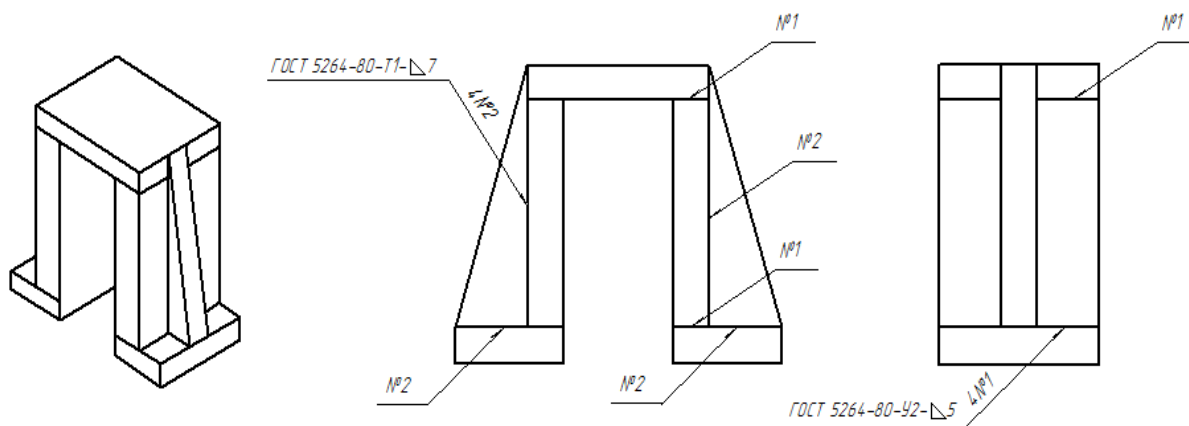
Пример выполнения чертежа сварного соединения (сварные швы на чертеже повторяются)
